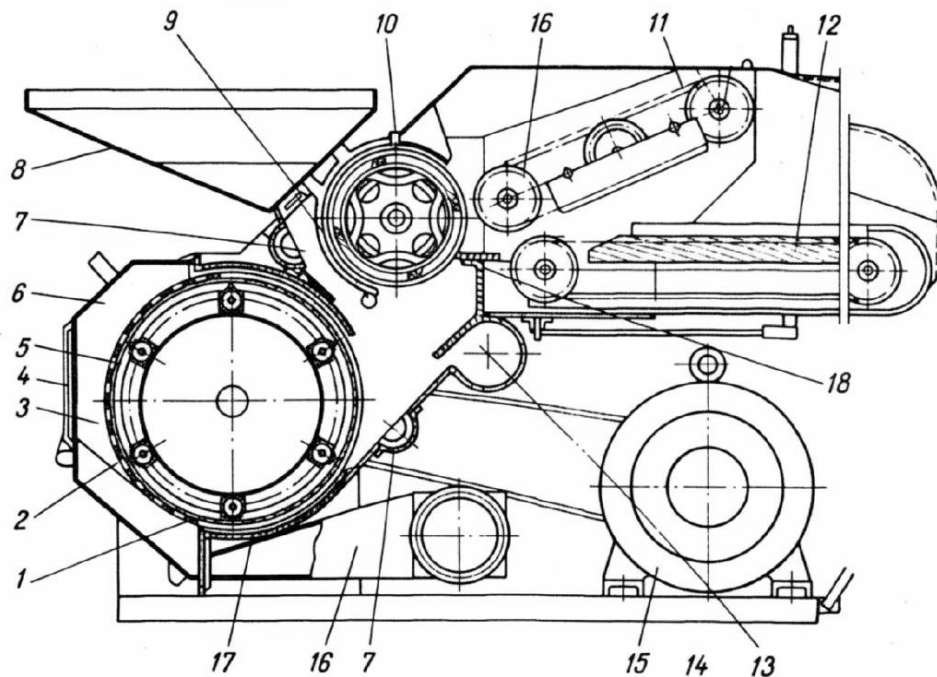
Схема дробарки КДУ-2 (розріз): 1 – дробильний барабан; 2 – змінне решето; 3 – ґратована камера; 4 – люк викиду; 5 – вставна викидна горловина; 6 – кришка дробильної камери; 7 – магнітний сепаратор; 8 – ківш-бункер для сипучих кормів; 9 – патрубок для води; 10 – ріжучий барабан; 11 – транспортер, що підпресовує; 12 – транспортер, що живить (подає); 13 – приймальний повітряний патрубок; 14 – рама; 15 – електродвигун; 16 – патрубок вентилятора, що відсмоктує; 17 – дека; 18 – протиризуча пластина.
